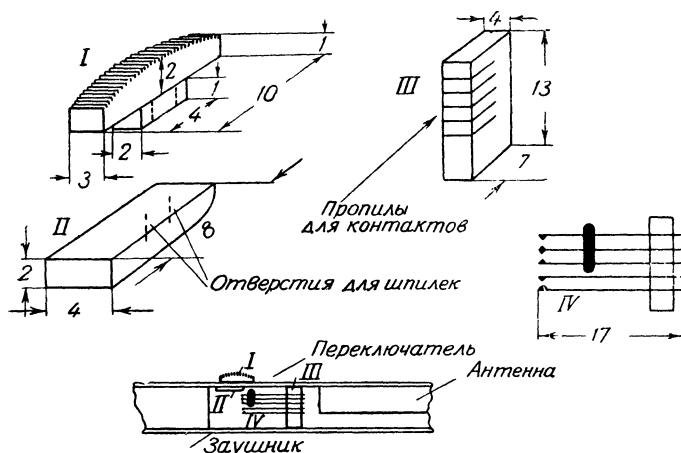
Переключатель рода работ: I — головка движка; II — движок; III — станина для контактов; IV — контакты в сборе; V — установка переключателя в заушнике
